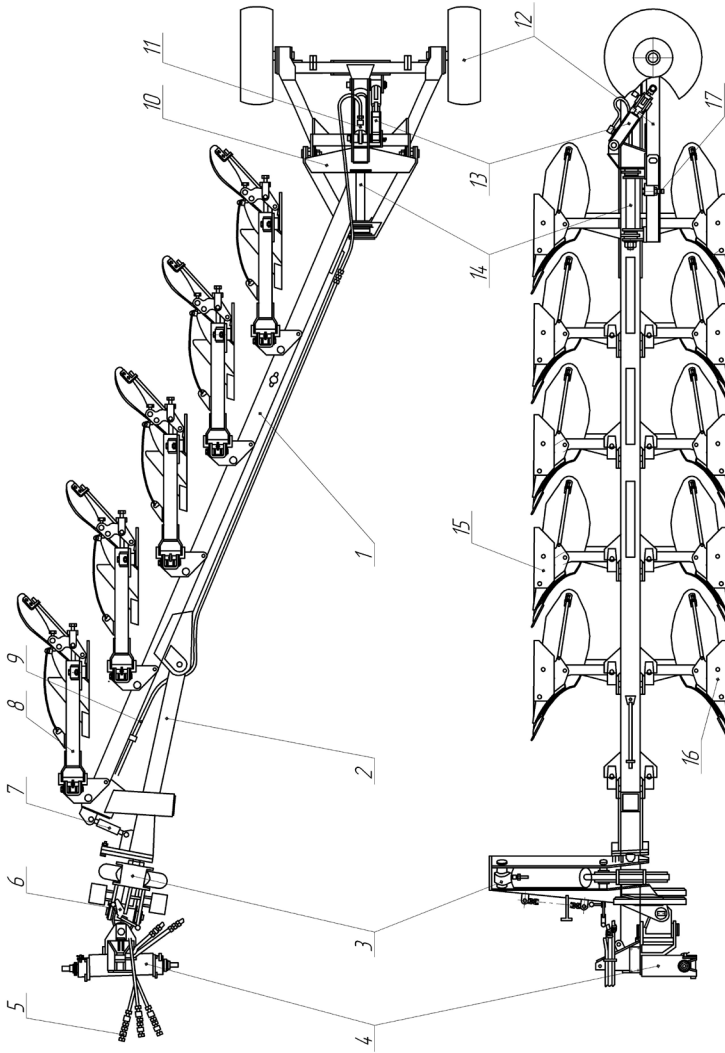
Плуг полунавесной оборотный ШО-5-40: 1 – рама; 2 – тяговая балка; 3 – механизм оборота рамы; 4 – навеска; 5 – гидросистема; 6 – фиксатор; 7 – тагрет; 8 – предохранитель; 9 – трубопровод; 10 – ось; 11 – гидrocилиндр; 12 – колесный ход; 13 – механизм регулировки глубины пахоты; 14 – рамка; 15 – левоборачивающий корпус; 16 – правоборачивающий корпус; 17 – регулировочный болт
